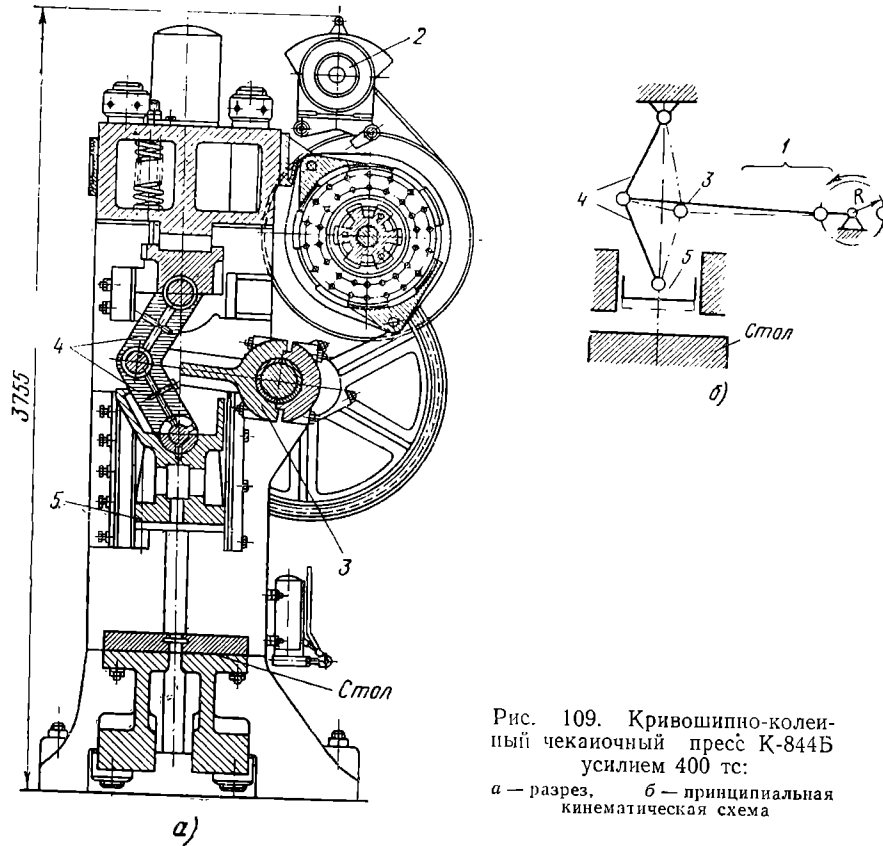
Кривошипно-колеиный чеканочный пресс К-844Б усилием 400 тс:
